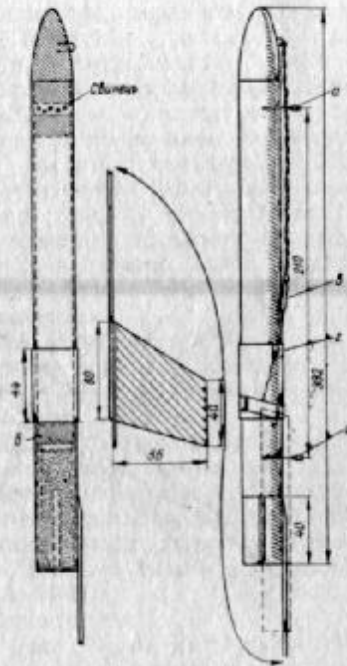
Креслення ракетоплана (вид збоку та розріз):
